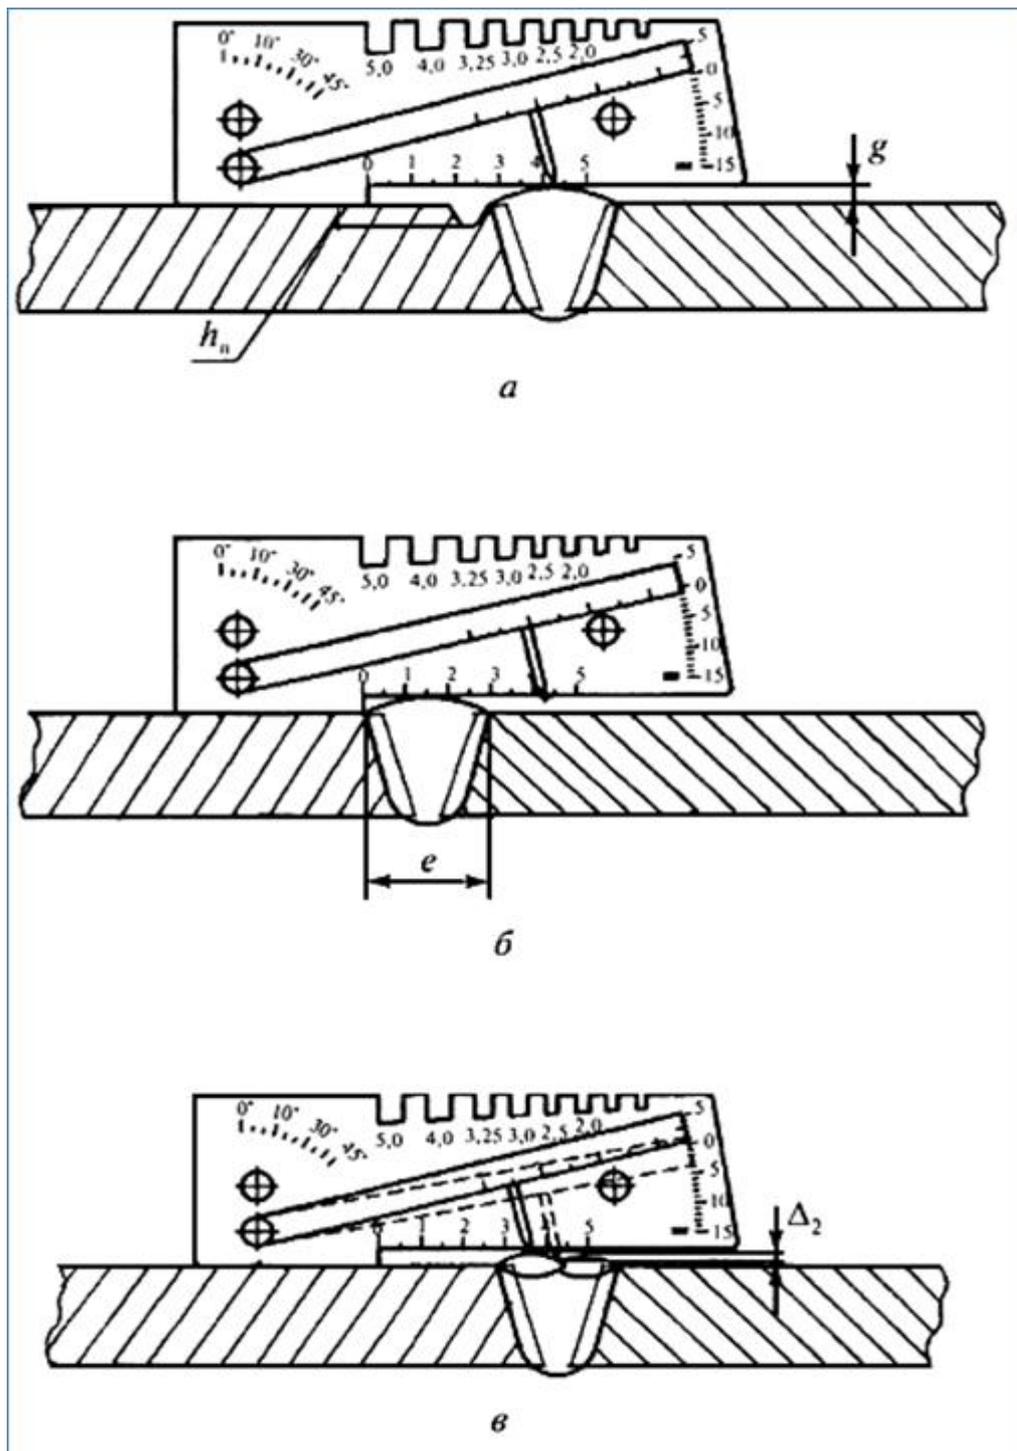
Измерения при помощи УШС-3: а - измерение высоты сварного шва и глубины подреза; б - измерение ширины сварного шва; в - измерение западаний между валиками сварных швов.
